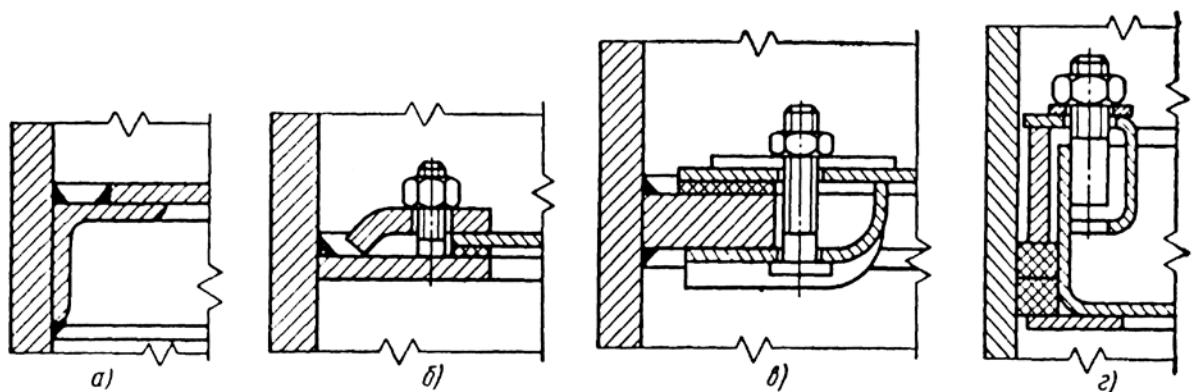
Варианты крепления полотна тарелки к корпусу:
